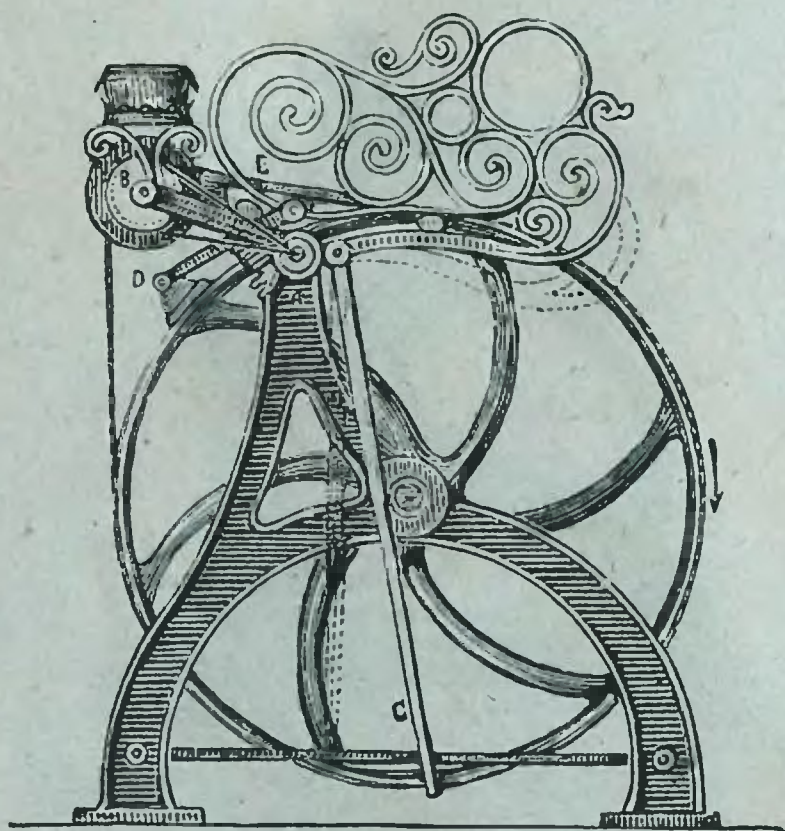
Объяснительный рисунокъ, дающій детали механизма.
